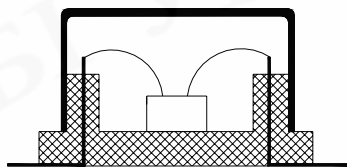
Корпус ИС на основе металлополимерной оболочки
